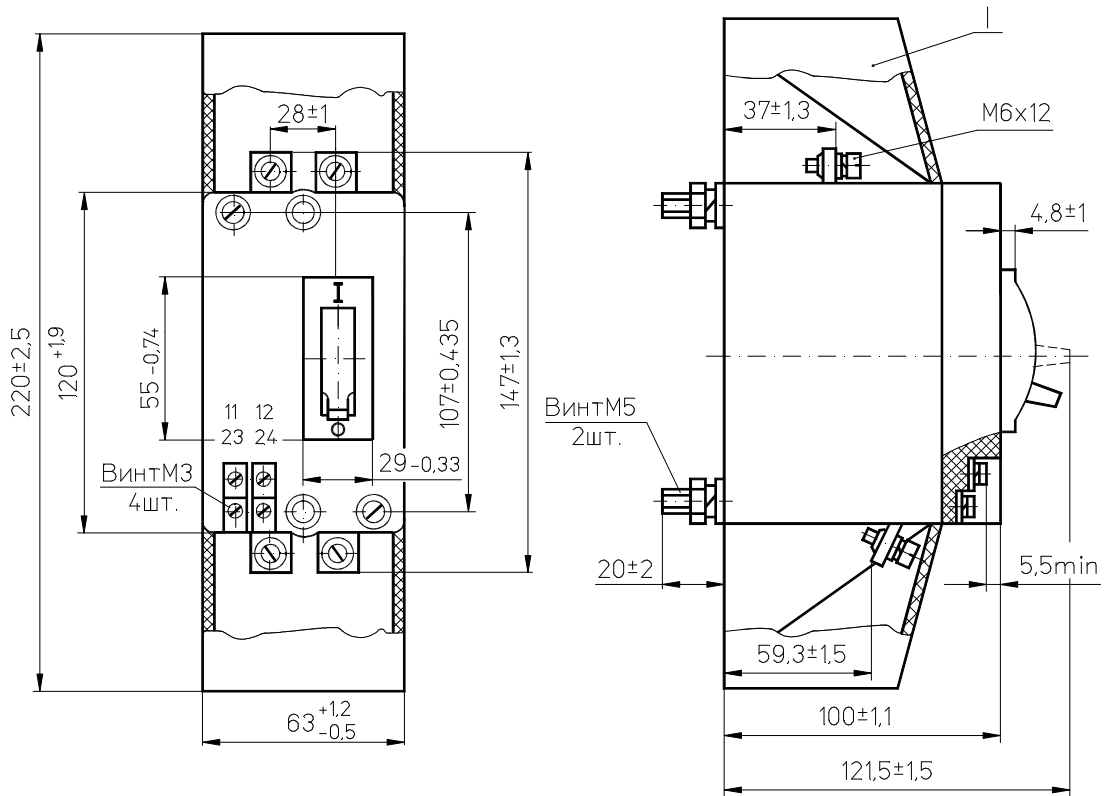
Сверление отверстий под винты крепления однополюсного выключателя
